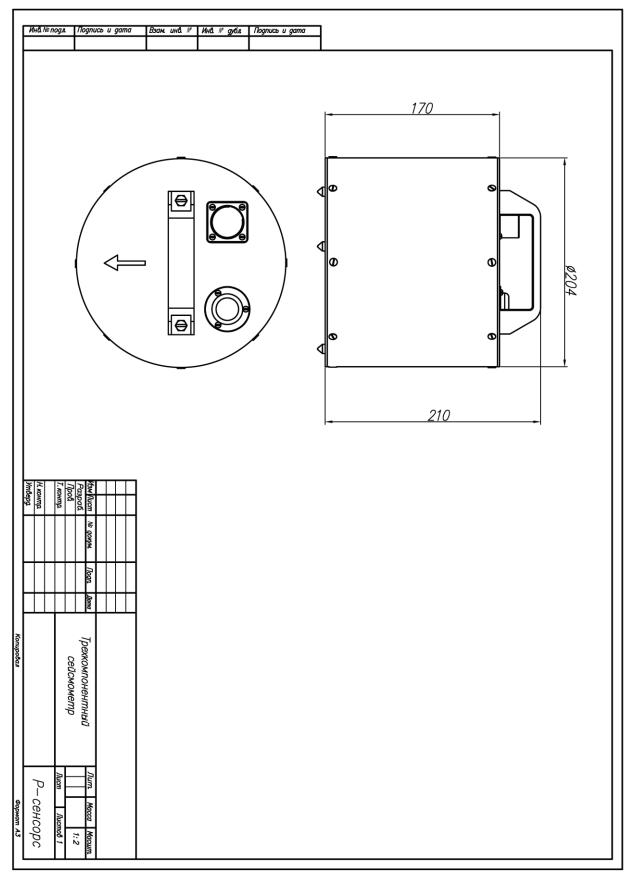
Габаритный чертеж сейсмометра СМЕ-6111.
